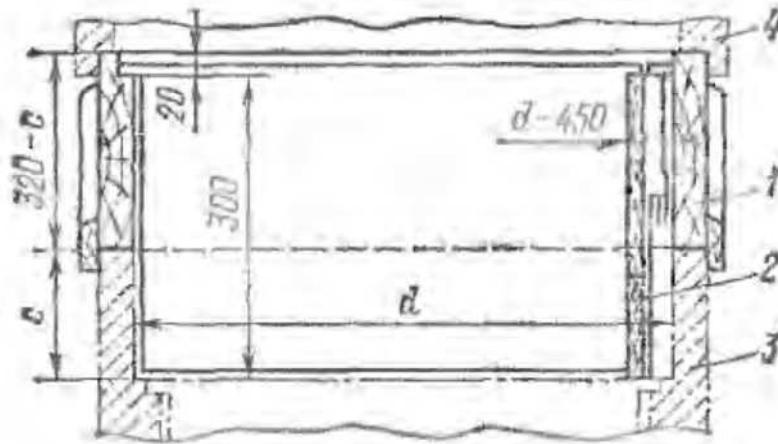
Верхний корпус для изготовления улья двухкорпусного с вкладышами с использованием обычных ульев, у которых стенки нижнего корпуса выступают над рамками на 10 мм, (размеры в мм):
